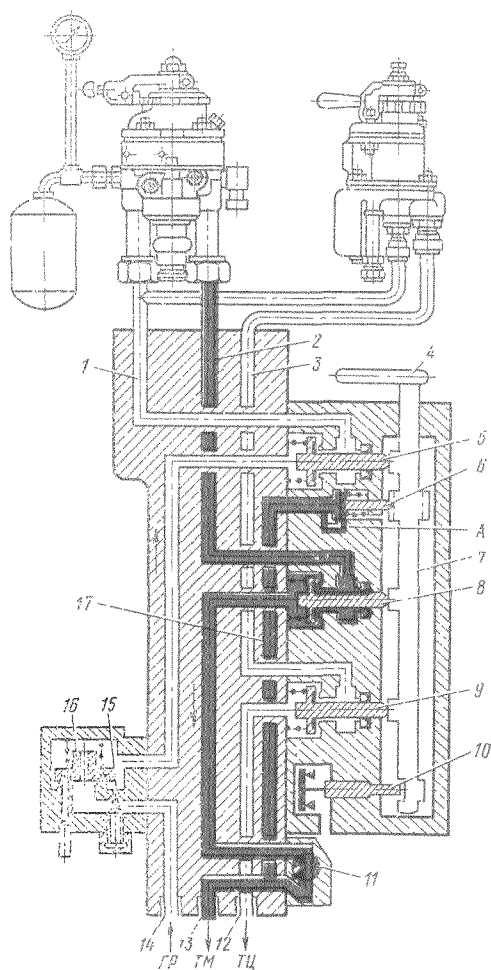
Схема устройства № 367М блокировки тормоза локомотива
